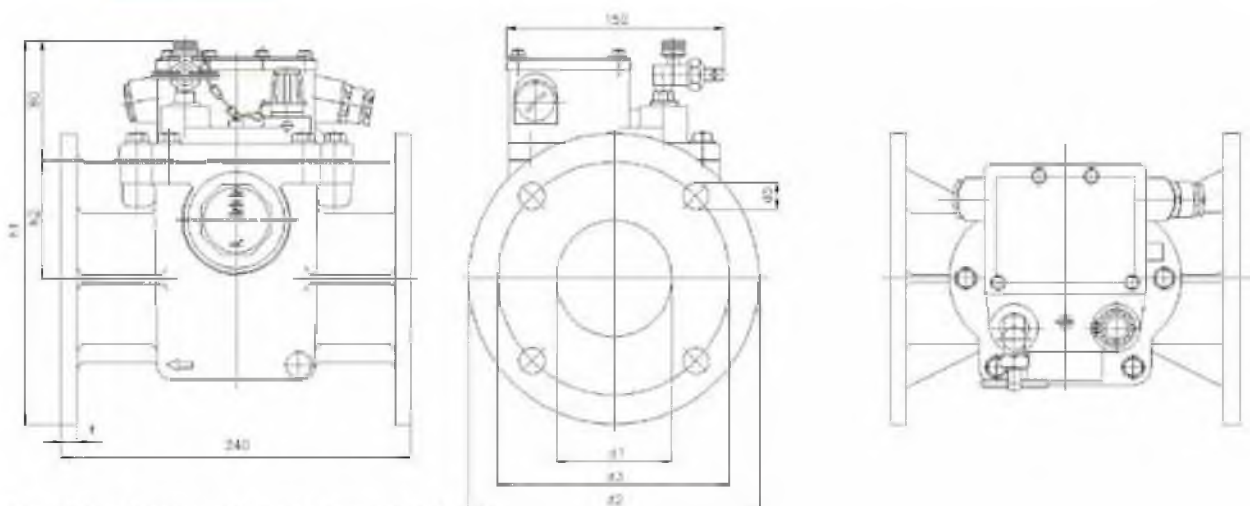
Размерный эскиз типов 41, 42, 43
